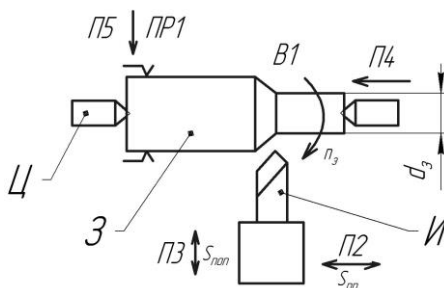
Схема рабочей зоны токарного гидрокопировального станка
